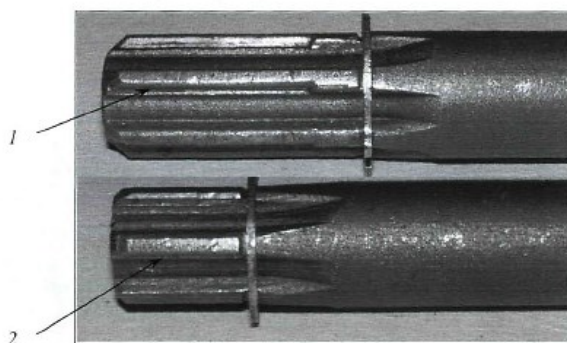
Вид изношенных поверхностей шлицев с разных сторон валика 700А.17.00.038-3: 1 – шлицевая часть вала, соединяемая с шестерней конического редуктора; 2 – шлицевая часть вала, соединяемая с туплкой привода насоса
